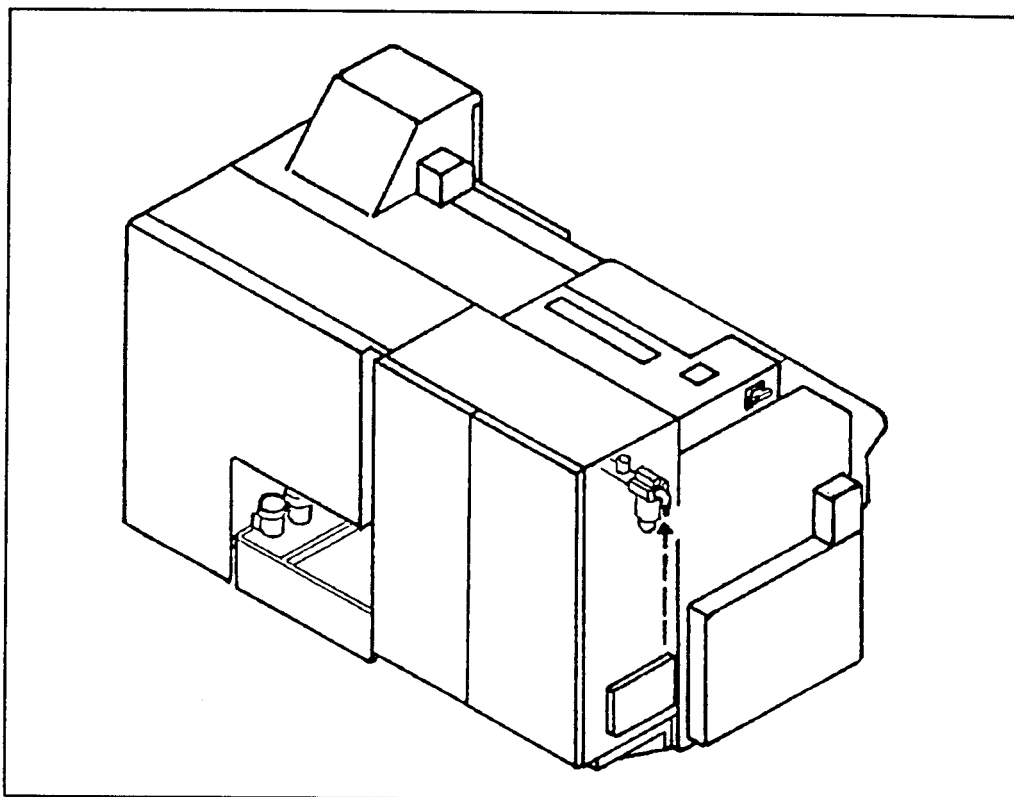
Przyłączenie kabla sieciowego (4/4)
